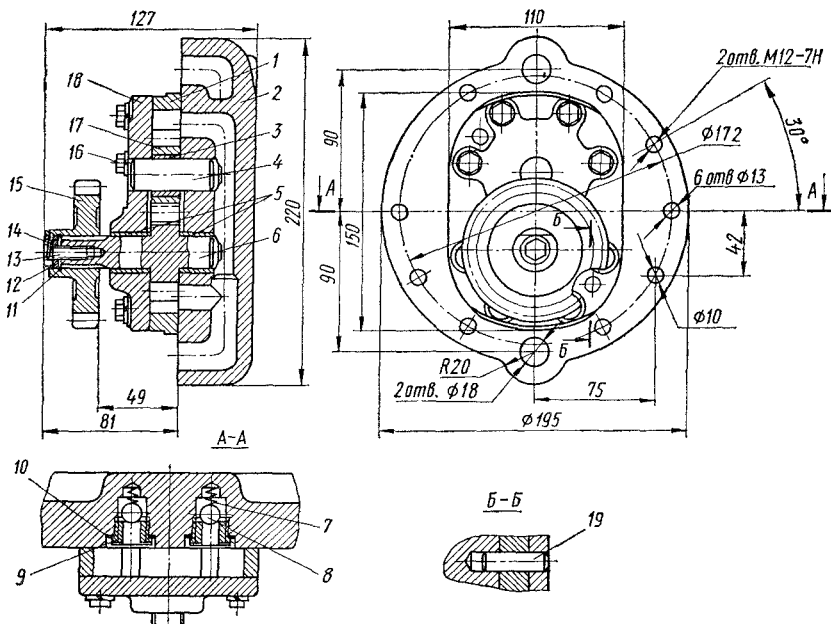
Насос шестеренный реверсивный НМШ-25Р:
